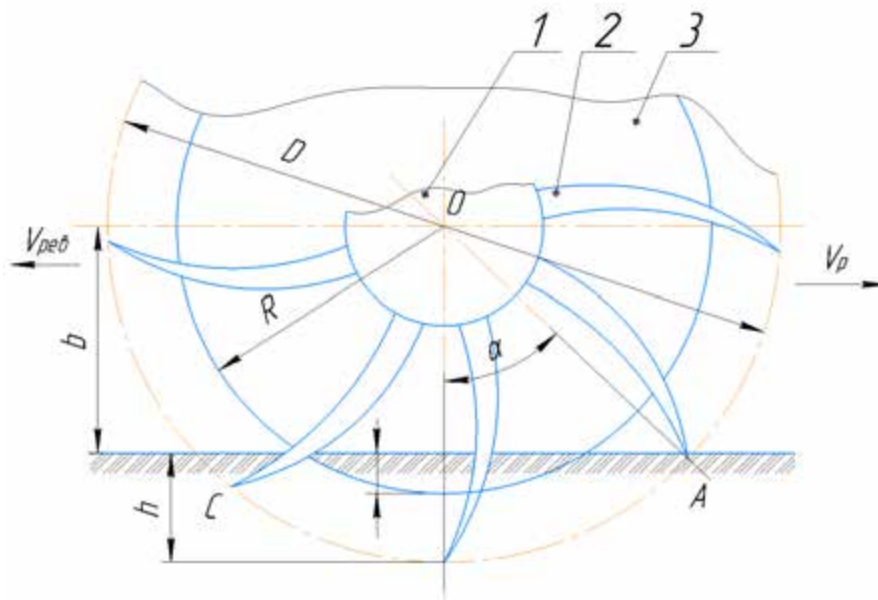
Розрахункова схема ротаційного зубового диска:
